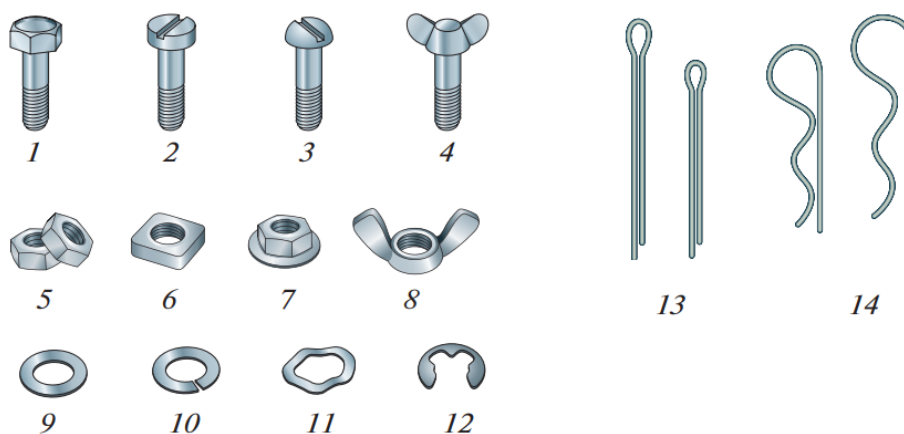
Крепёжные детали: 1 — болт с шестигранной головкой; 2 — винт с цилиндрической головкой; 3 — винт с полукруглой головкой; 4 — винт с барашковой головкой; 5 — гайка шестигранная; 6 — гайка квадратная; 7 — гайка шестигранная с фланцем; 8 — гайка барашковая; 9 — шайба плоская; 10 — шайба пружинная Гровера; 11 — шайба волновая; 12 — шайба быстросъёмная; 13 — шплинты прямые; 14 — шплинты пружинные
